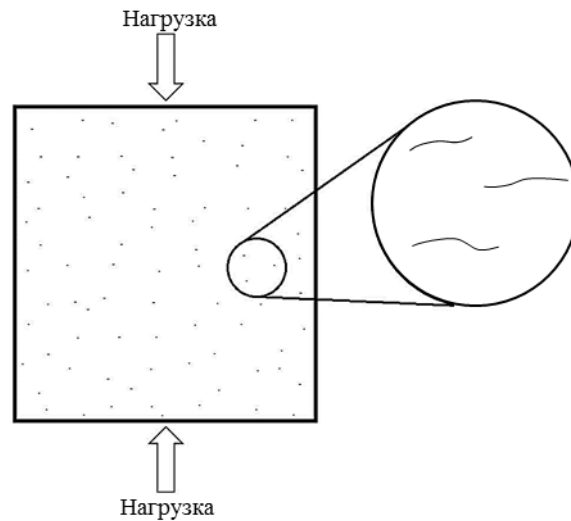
Схематичное изображение поперечного сечения прессовочной заготовки
